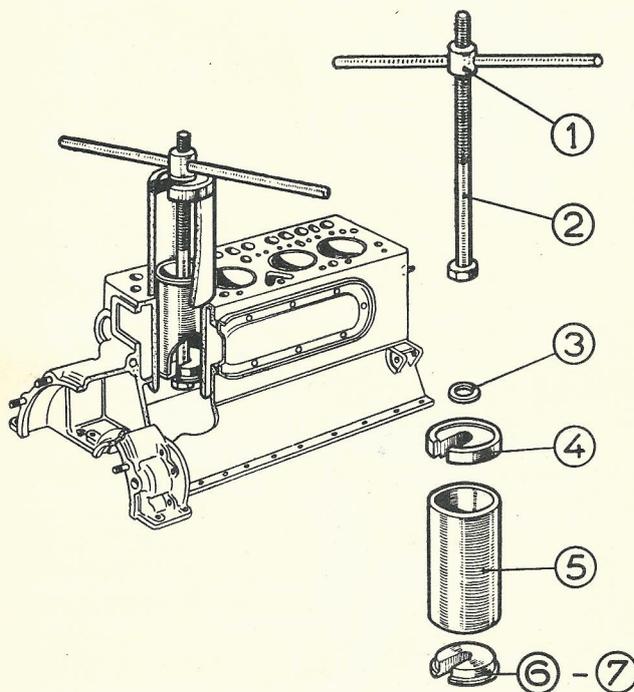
Typ 402. Demontage der Zylinderlaufbüchse.
